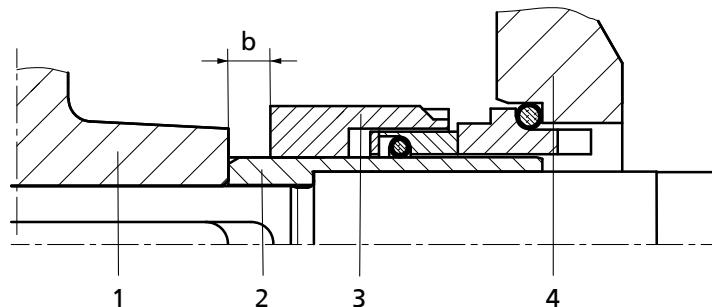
Tenuta meccanica - dimensione di montaggio b
